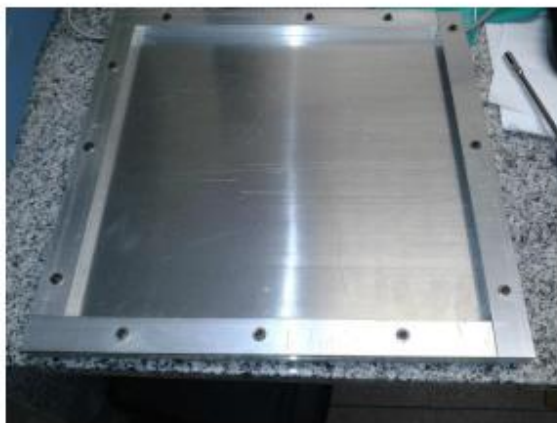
Molde fechado de alumínio para fabricação das placas. Fonte: (FERNANDES, 2014).
